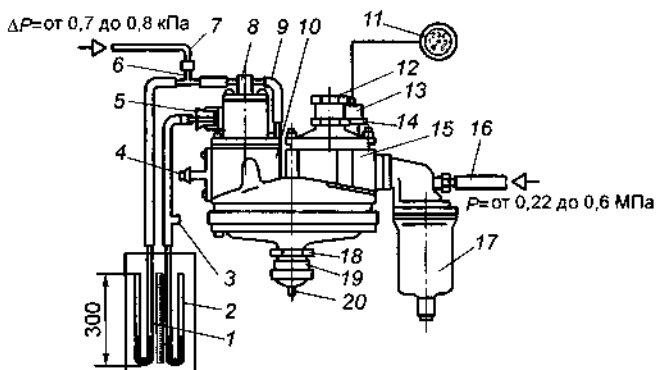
Схема проверки работы редуктора низкого давления с помощью переносных пьезометров: 1 — пьезометр для контроля вакуума в полости разгрузочного устройства; 2 — пьезометр для регулировки избыточного давления в полости второй ступени; 3 — отверстие для соединения с окружающей средой; 4 — заглушка в патрубке крышки; 5 — пробка с трубкой в патрубке дозирующего экономайзерного устройства; 6 — тройник; 7 — трубка для передачи разрежения в полость разгрузочного устройства; 8 — крышка дозирующего экономайзерного устройства; 9 — шланг для передачи разрежения в полость разгрузочного устройства; 10, 15 — соответственно вторая и первая ступени редуктора; 11 — манометр в кабине водителя; 12 — регулировочная гайка; 13 — датчик манометра; 14, 18 — контргайки; 16 — шланг для подвода сжатого воздуха в полость первой ступени; 17 — корпус газового фильтра; 19 — регулировочный ниппель; 20 — стержень
